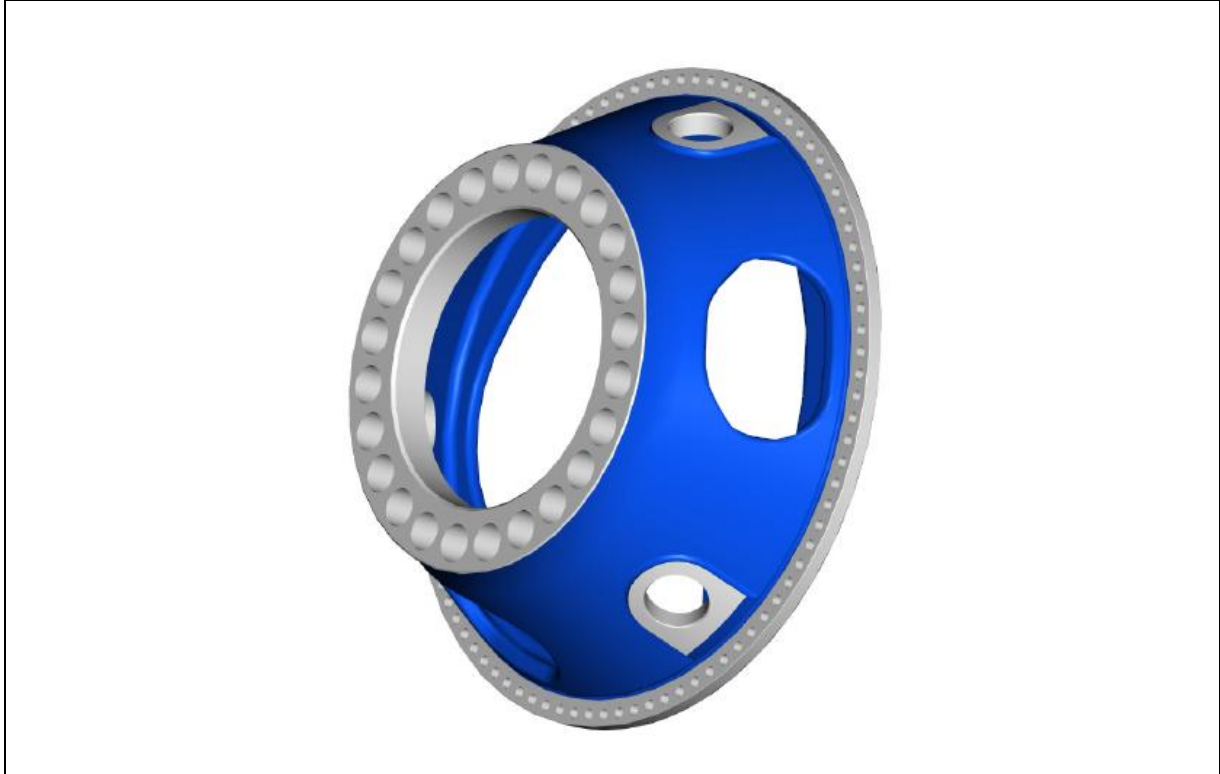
Variante 1: Bearbeitungsflächen in grau / Variant 1: machining surfaces in gray
